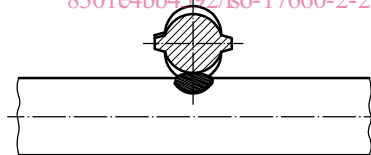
Assemblage en croix soudé par les procédés 21 et 23
